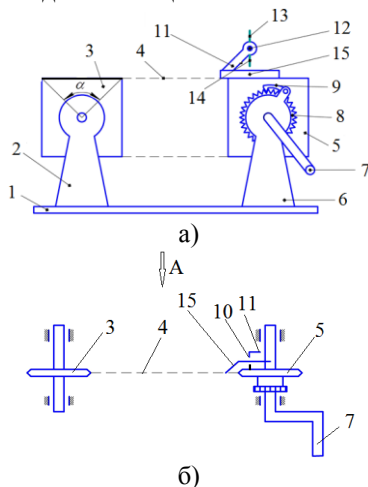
Лабораторная установка для демонстрации изменения скорости движения приводной цепи
